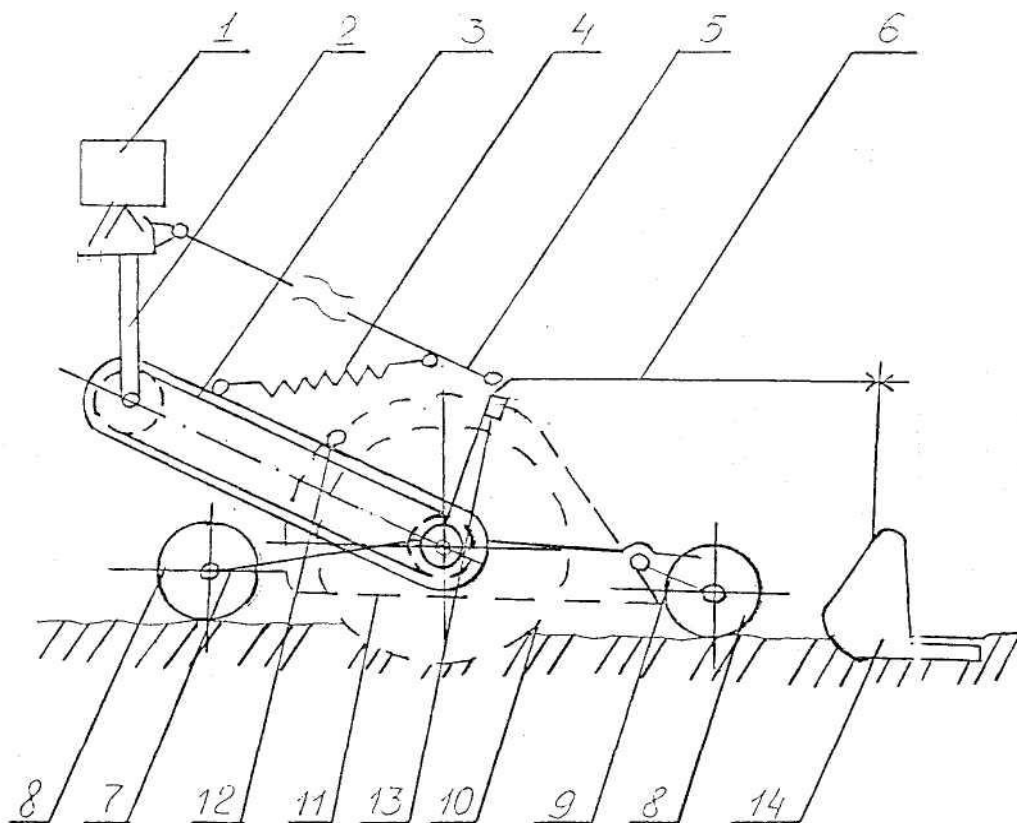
Схема секції фрезерно-лапового культиватора
